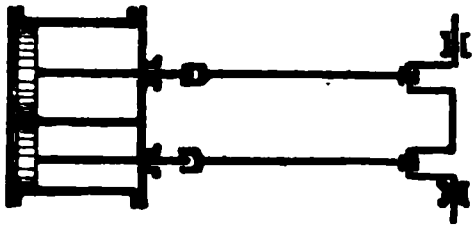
Woolfsche Maschine mit gleichgerichtetem Kolbenlauf. Bei den Woolfschen Maschinen arbeitet der Niederdruckcylinder stets ohne Expansion.
